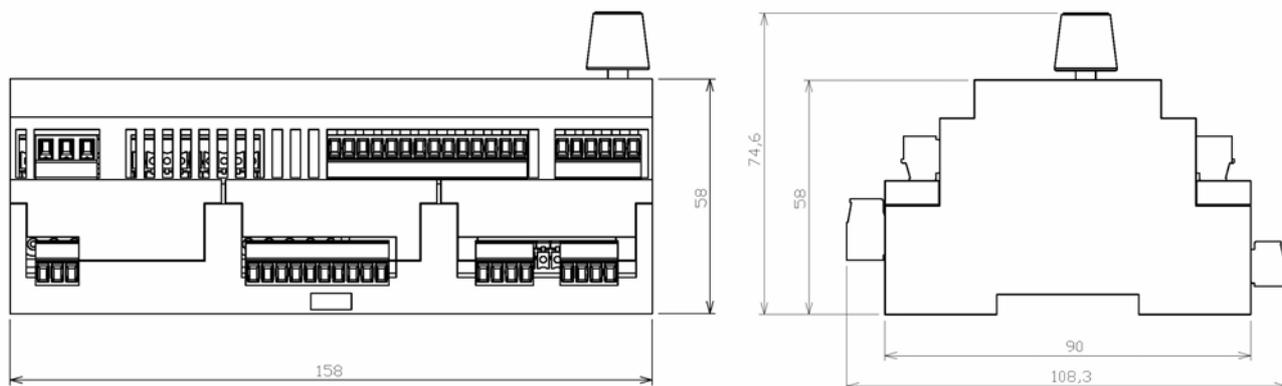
Dimensioni serie Robur Box: vista frontale e laterale
